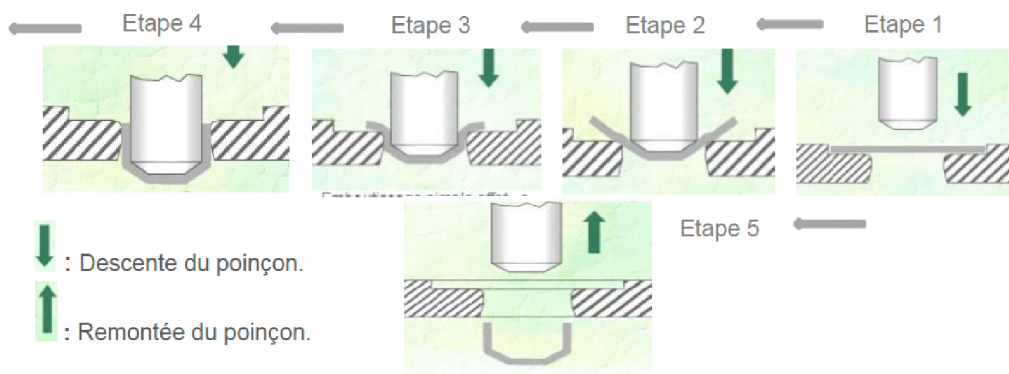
Principe du travail d'un Outil d'Emboutissage Sans Serre-Flan.
